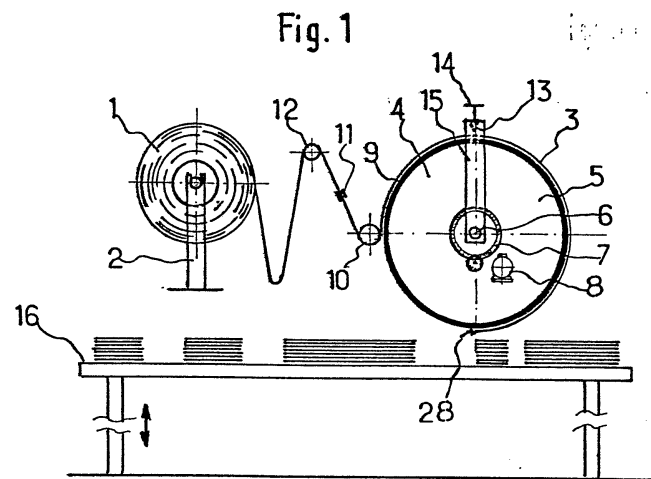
Exemple de machine de coupe horizontale.
